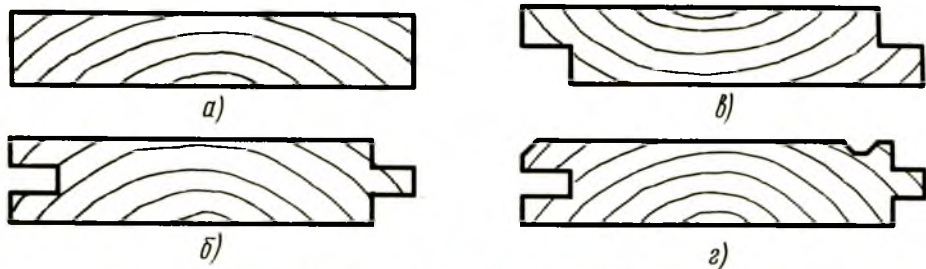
Основные профили по сечению фрезерованных заготовок:
